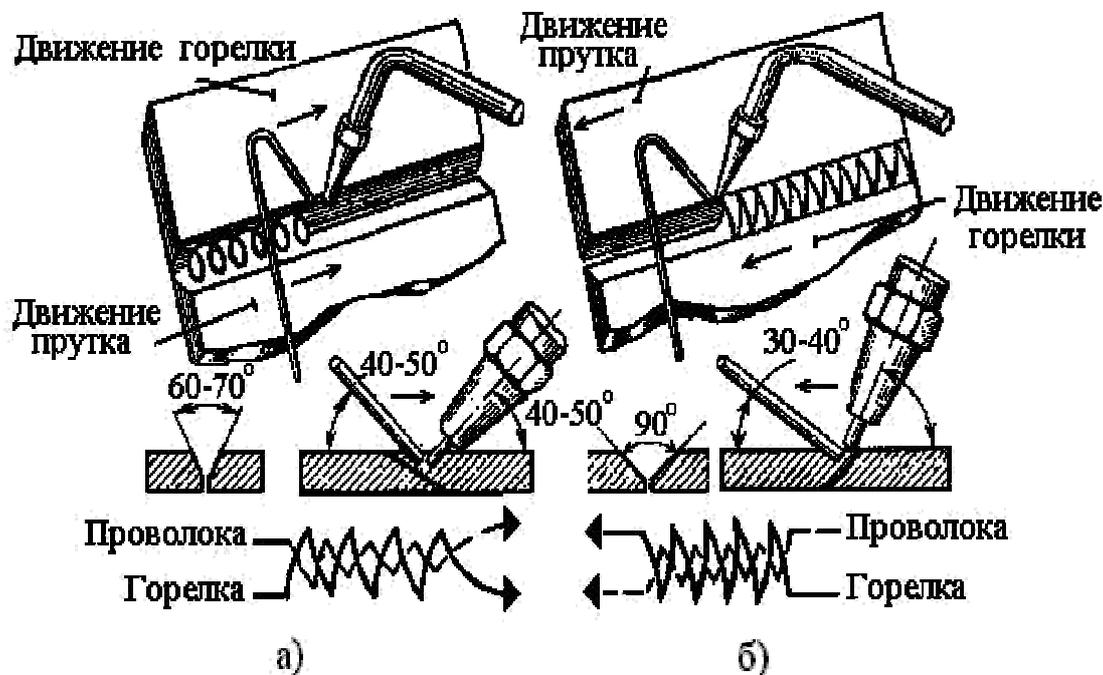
Способы газовой сварки: а- левый; б – правый.
